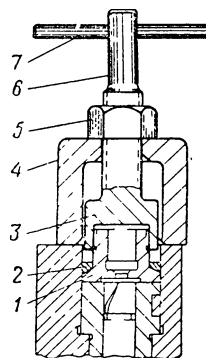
Приспособление для выпрессовки корпуса нагнетательного клапана:
